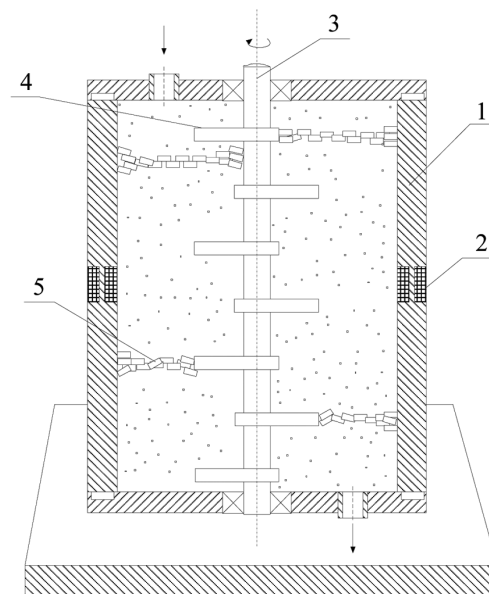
Конструктивная схема смесителя ЭМС-1 (Патент России на полезную модель № 653): 1 – корпус; 2 – обмотка управления (ОУ); 3 – ротор; 4 – кольца из ферроэласта; 5 – цилиндрические ферромагнитные мешалки
